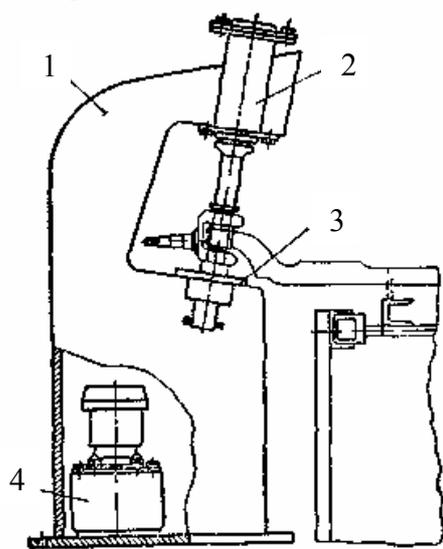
Специальный гидравлический пресс для выпрессовывания шкворней: 1 – станина; 2 – гидроцилиндр; 3 – установочный стол; 4 – насос
